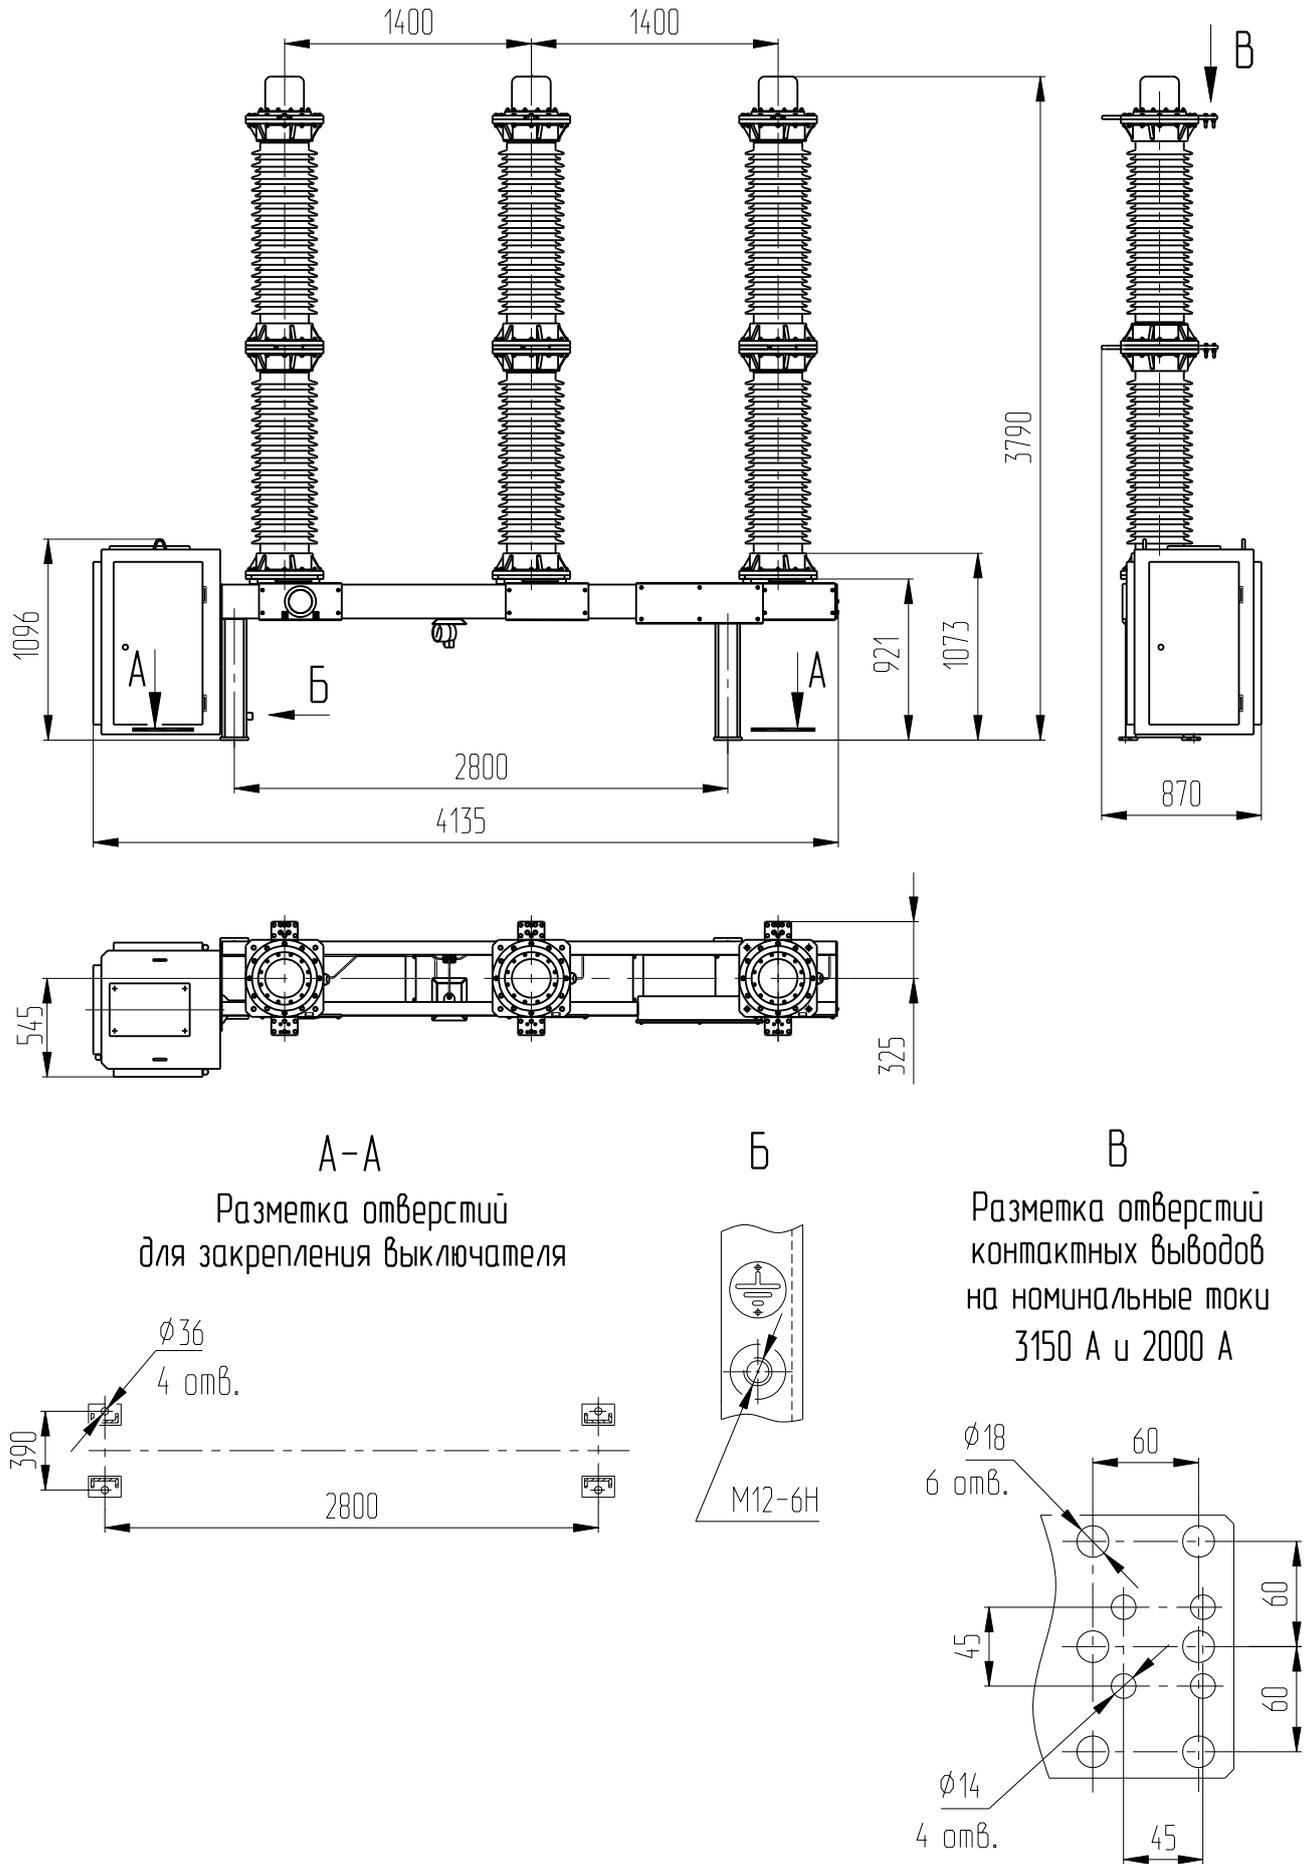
Габаритные, установочные и присоединительные размеры выключателя
